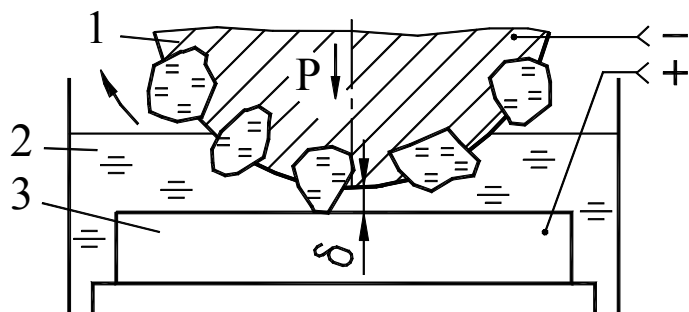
Схема электроалмазного шлифования: 1 – шлифовальный круг; 2 – электролит; 3 – заготовка; δ – зазор; P – давление
